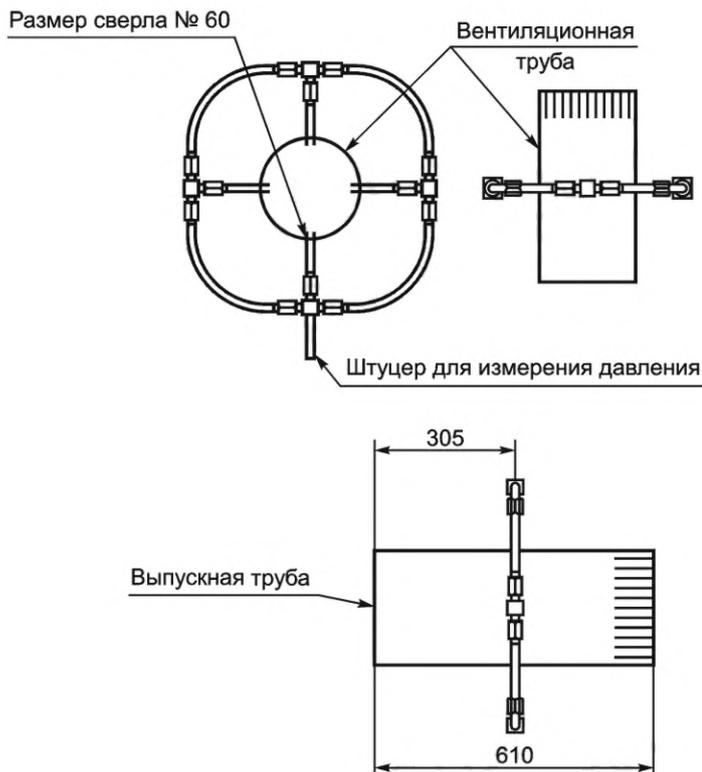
Пьезокольцо и детали типичной конструкции
